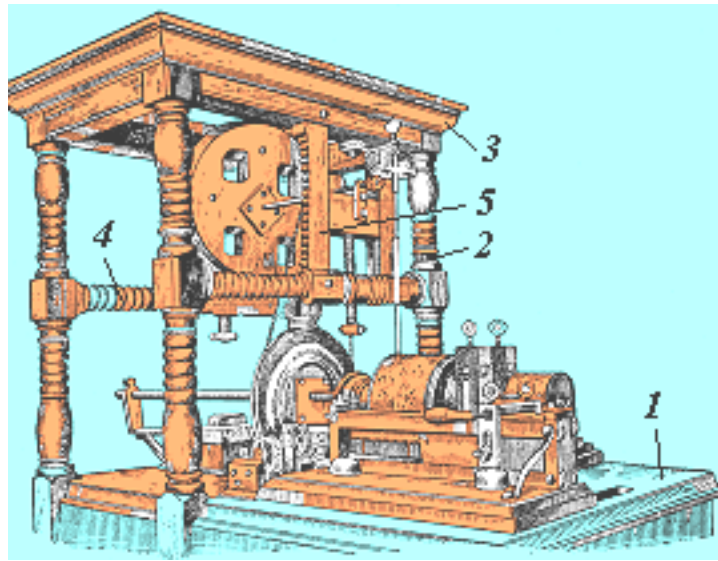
а. Токарно-копировальный станок (1712 г.): общий вид
